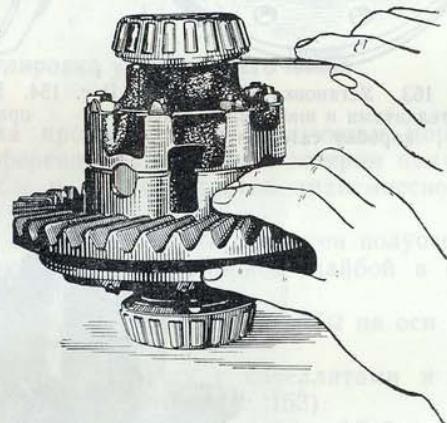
Замер щупом зазоров при регулировке подшипников дифференциала
